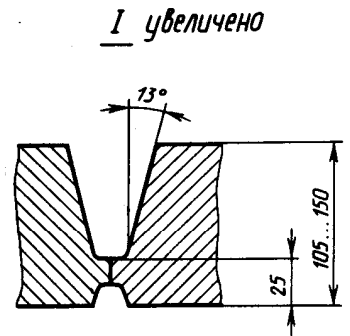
Способы сварки патрубков в корпус реактора
